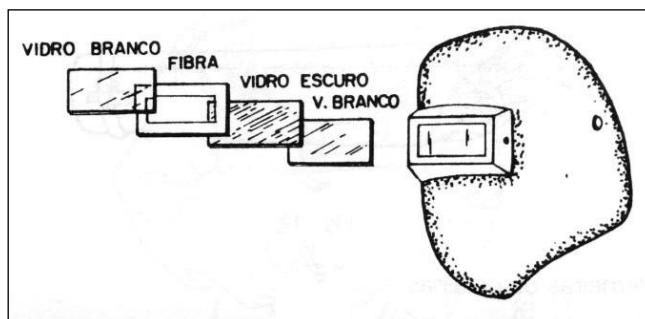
Montagem de Vidros na Máscara de Solda.
